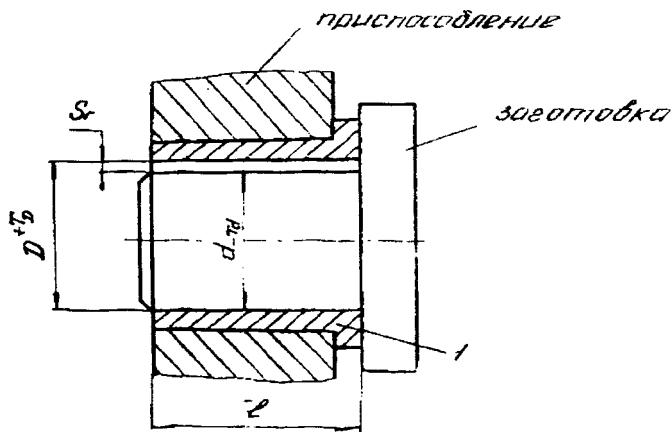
Схема базирования заготовки в цилиндрическом отверстии
